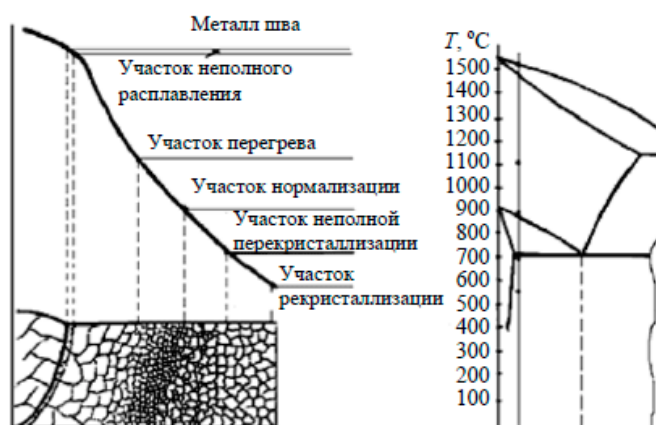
Строеие ЗТВ при сварке низкоуглеродистой стали.
